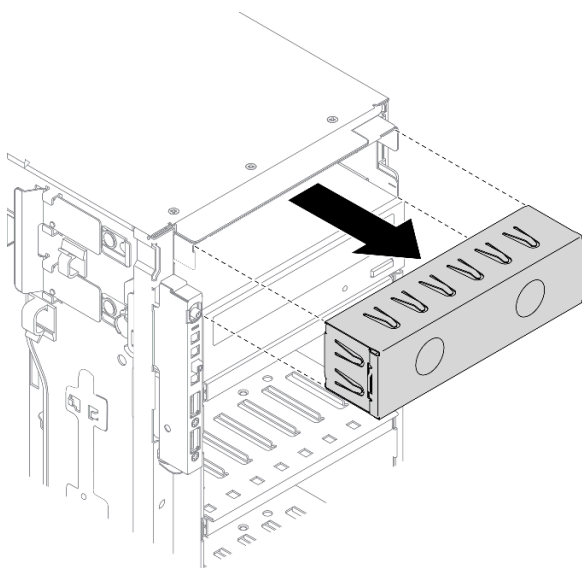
Installazione dell'elemento di riempimento del vano dell'unità
